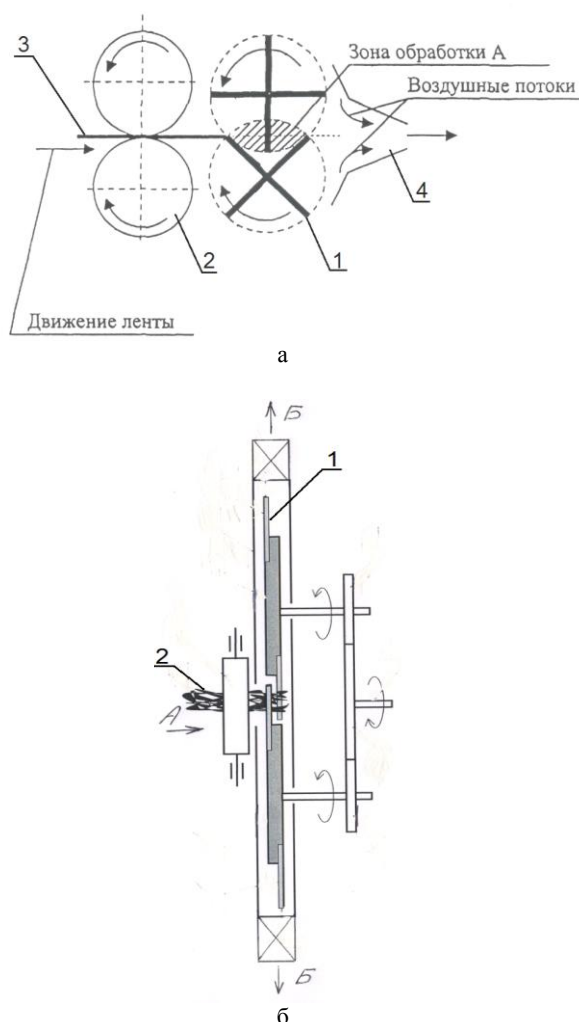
Устройство для поперечного расщипывания волокна в ленте, движущейся параллельно линии зажима: а – вид сбоку; б – вид сверху
